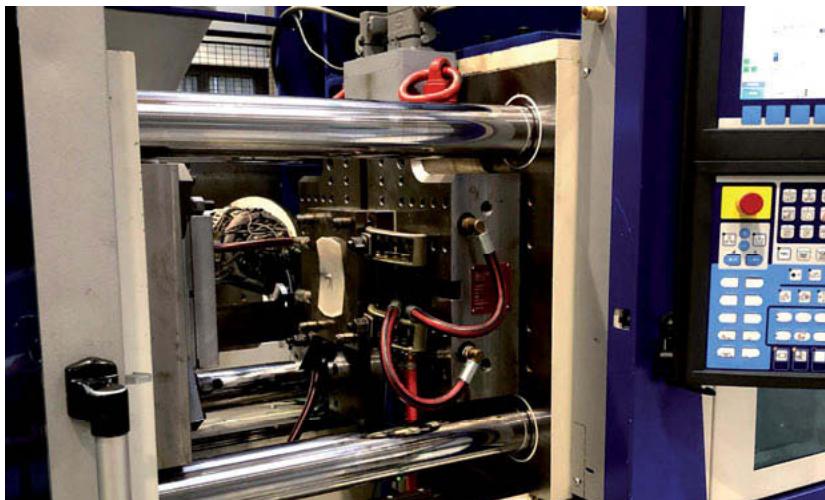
Eingebaute Zwischenplatte 600 x 600 x 136 mm mit Werkzeug für das Sandwich-Spritzgießen in die Spritz-gießmaschine KM 80-380CX mit KM 390 Bolt-On Seiten-Spritzaggregat an der TU Chemnitz
